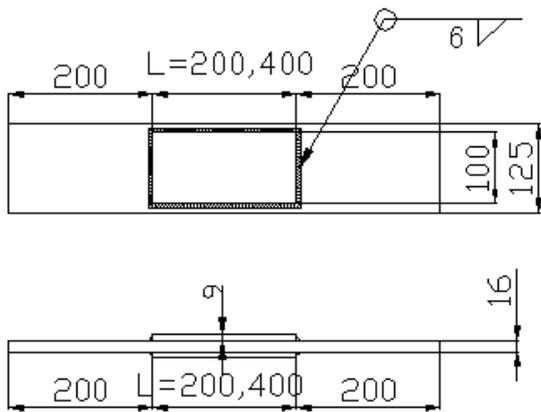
カバ - プレートすみ肉溶接継手の形状・寸法
